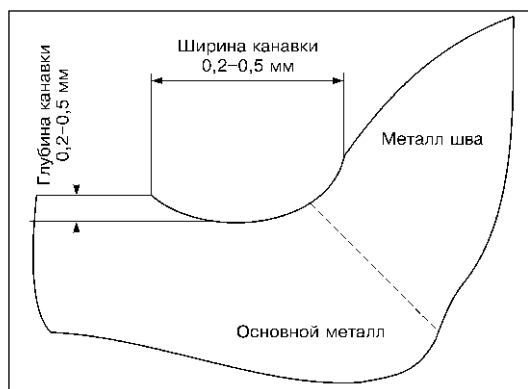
Профиль сварного шва после упрочнения ВМП зоны сплавления шва с основным металлом
